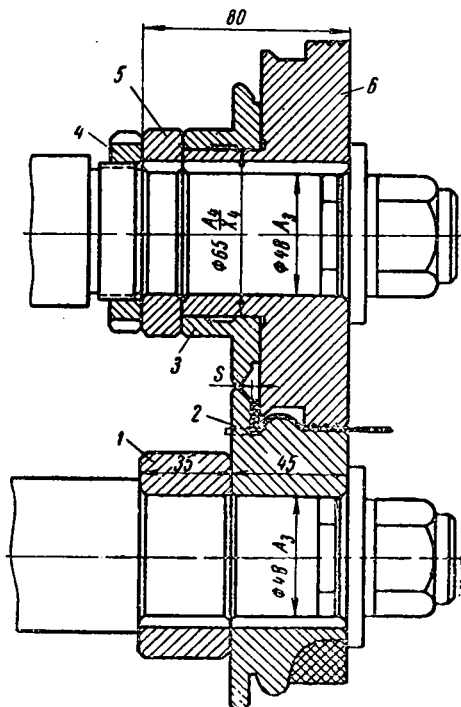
Комплект роликов для офланцовки звеньев воздухопроводов фланцами из полосовой стали
